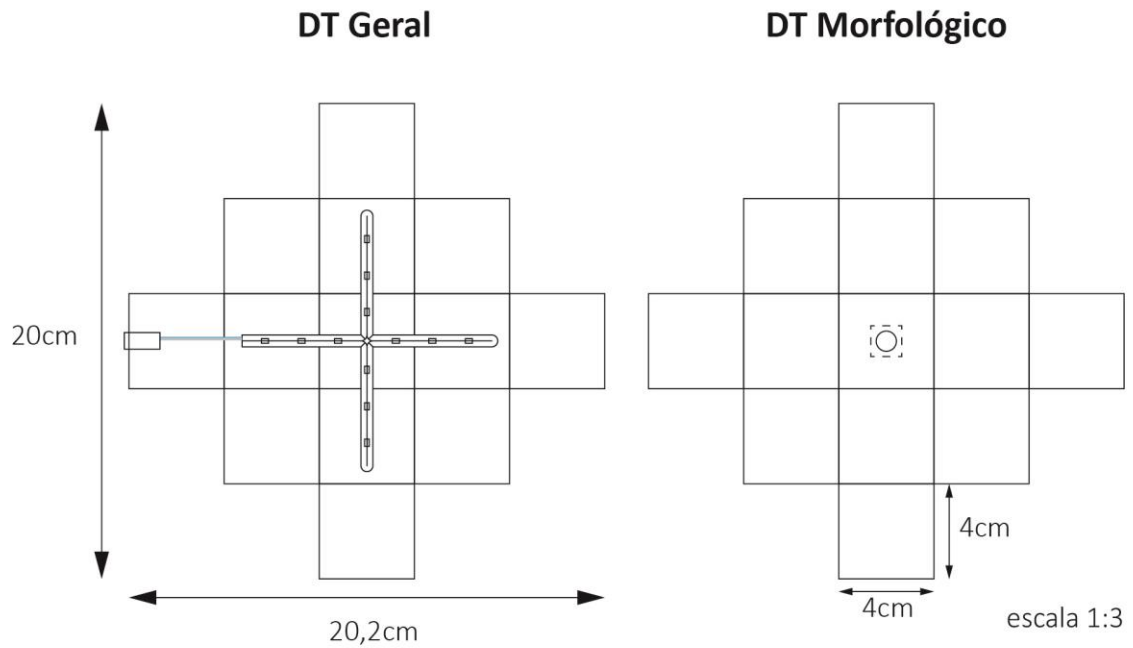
Desenho Técnico corte e vinco do Abajur Médio
